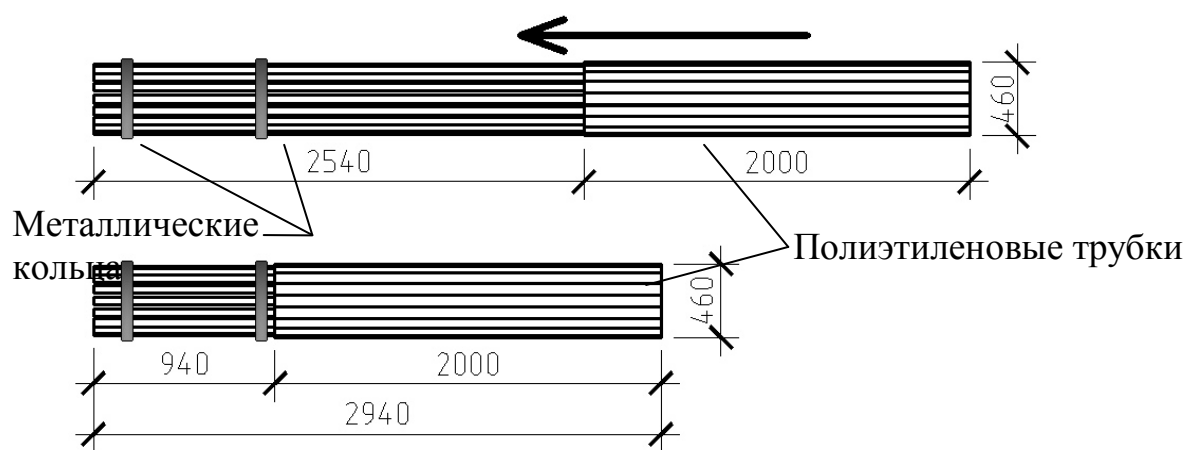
Размеры конструкции с выдвинутыми телескопическими трубками и в положении для транспортировки
